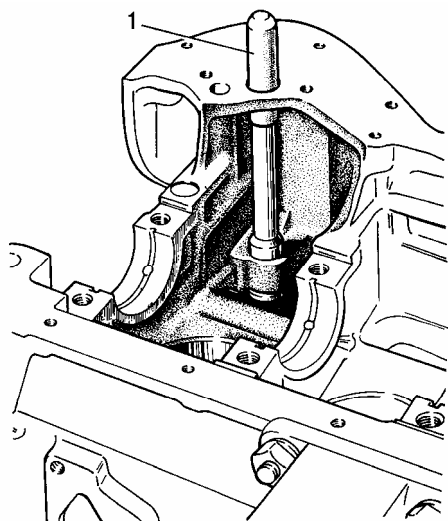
Выпрессовка втулки шестерни привода масляного насоса и распределителя зажигания:
